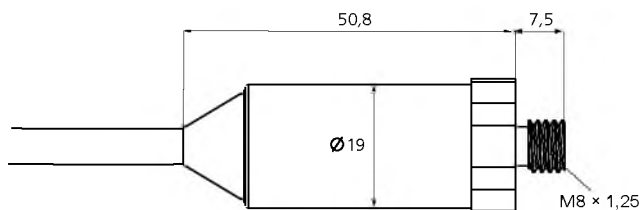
Габаритный размеры датчика с диапазоном измерения до 40 бар
